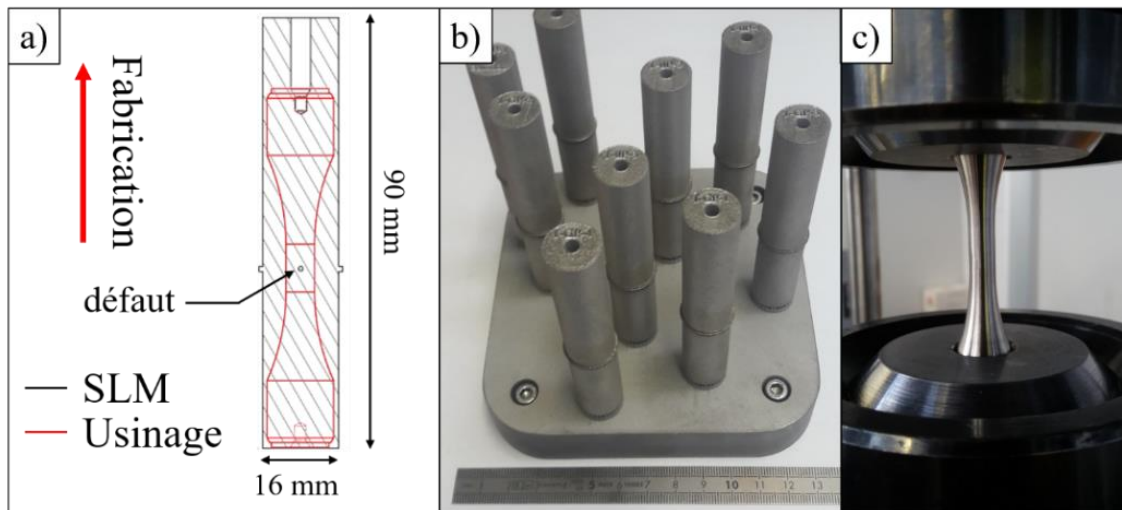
a) Plan du cylindre avec défaut centré et de l'éprouvette de fatigue b) Cylindres après fabrication SLM c) Éprouvette usinée montée sur vibrophore
